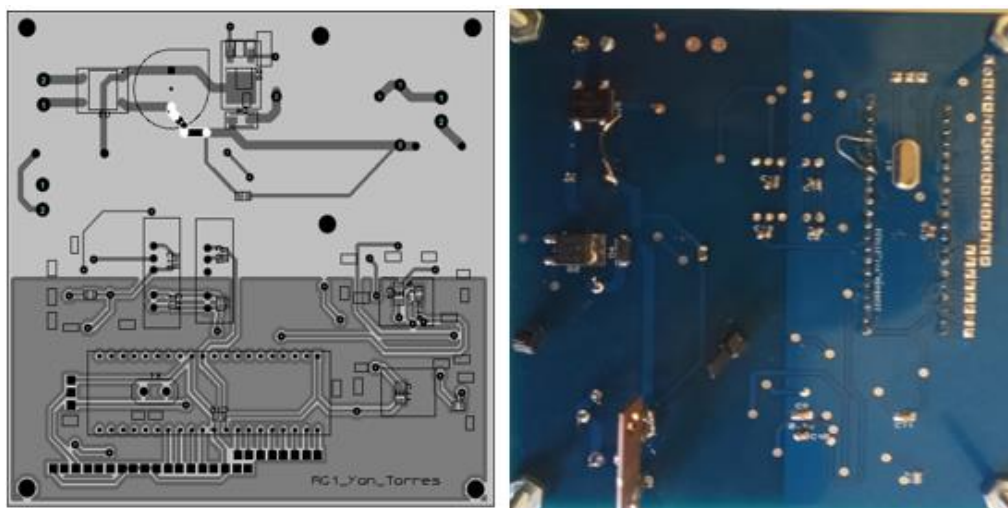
Diseño y montaje de la tarjeta vista inferior. (Fuente: autor)
